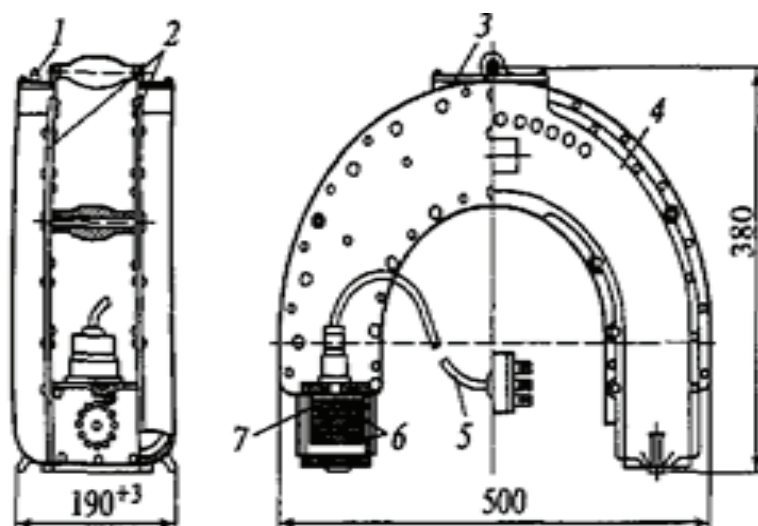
Магнитно-порошковый дефектоскоп: 1 — выключатель, 2 — сердечник, 3 — клеммовый щиток, 4 — корпус, 5 — трехжильный кабель, 6, 7 — намагничивающая и дополнительная катушки
